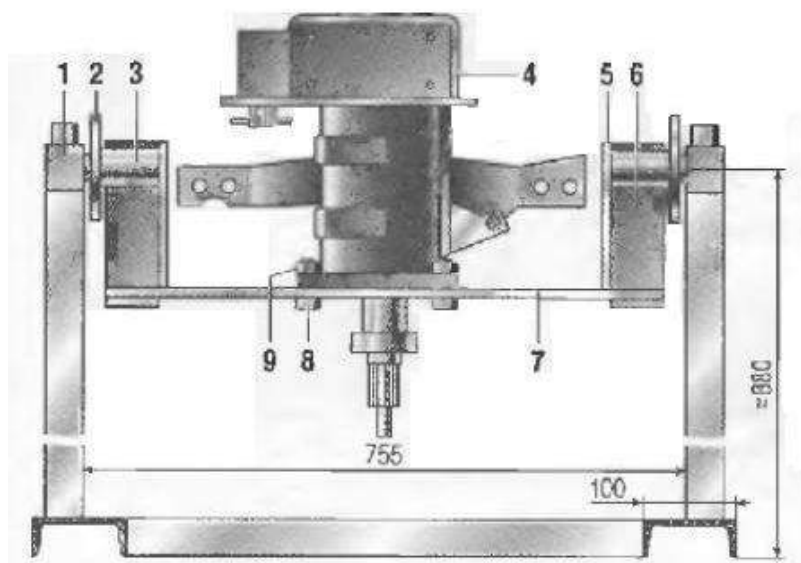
Пристосування для ремонту коробок передач і редукторів: 1 – Універсальний стенд; 2 – Диск; 3 – Цапфа; 4 – Коробка передач; 5, 6 – Листи; 7 – Траверса; 8 – Болт; 9 – Гайка.
